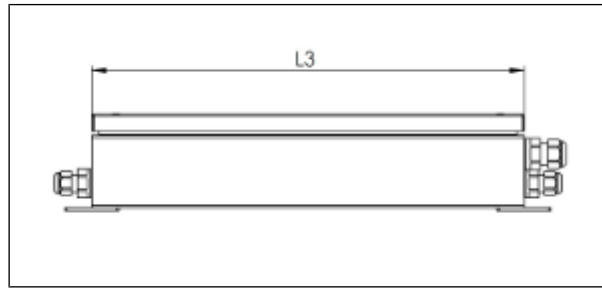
Längsseitenansicht mit Abmessungen der TSG V4-Elektronik extern
